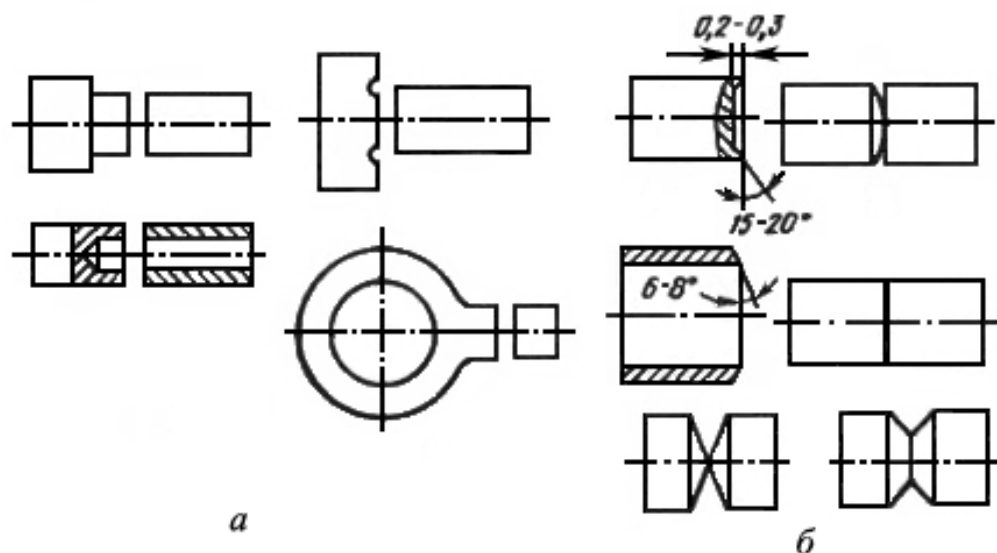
Рациональная конструкция соединений для стыковой сварки:
